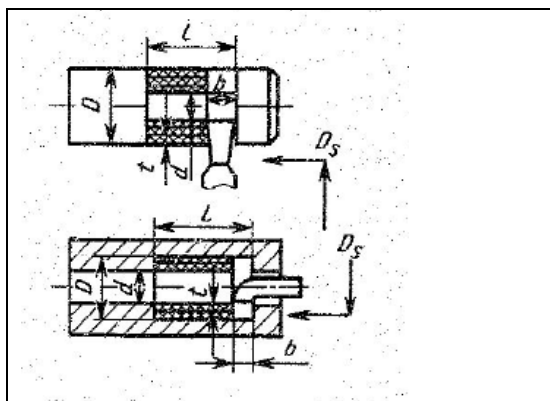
Схемы точения наружных и внутренних выточек поперечной и продольной подачей
